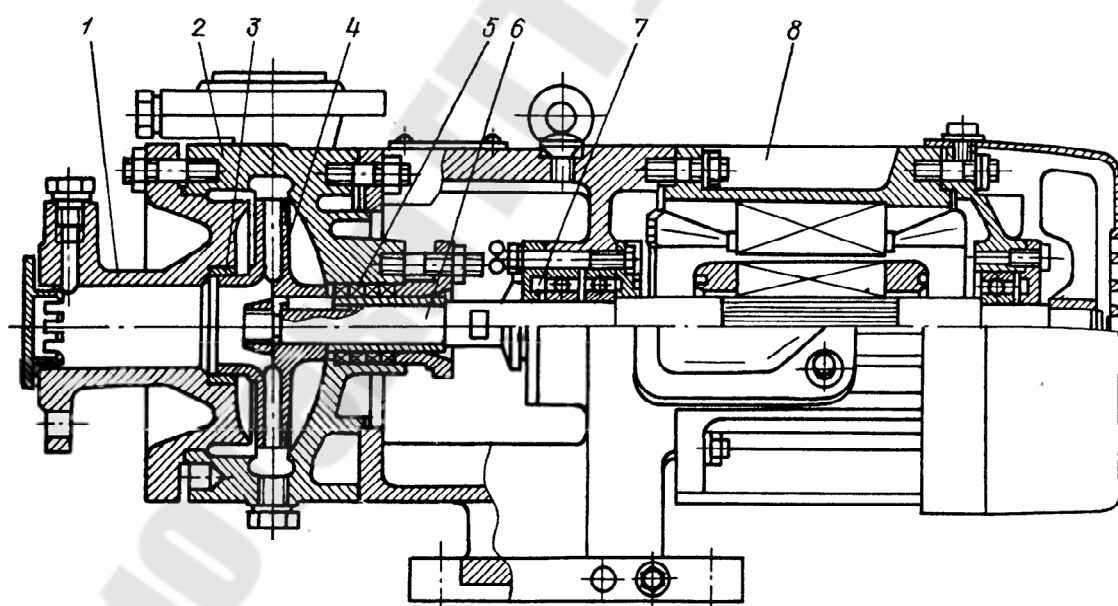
Центробежный одноступенчатый горизонтальный
